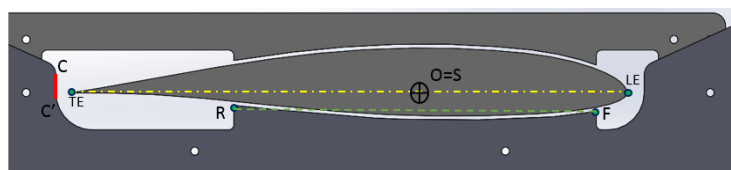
Secondo progetto del sistema Power VTOL
